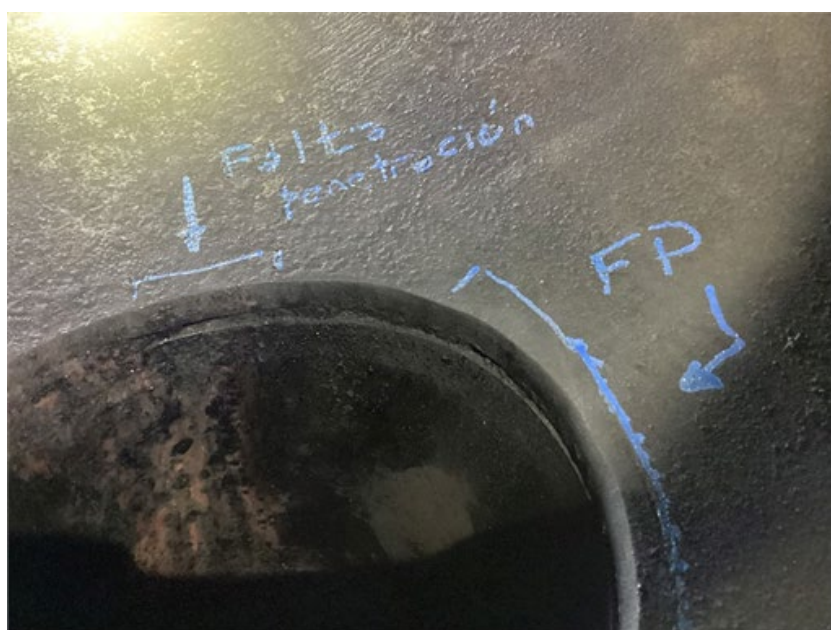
Falta de penetración en soldadura interna de acometida
